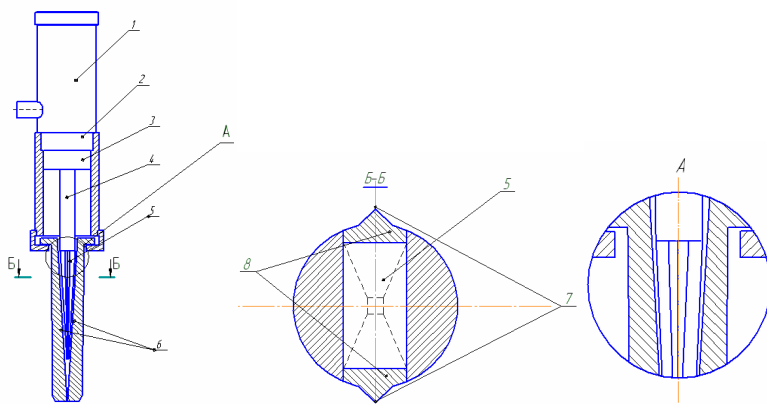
Гидроклиновое оборудование для реконструкционных работ (с дополнительными щеками)
